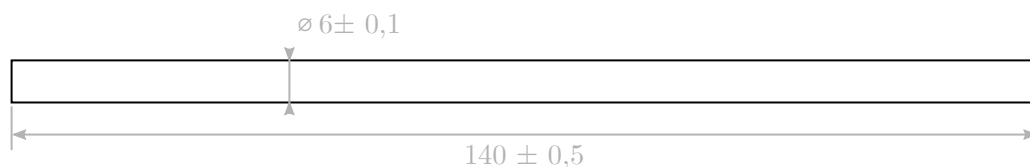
Dimensions géométriques des éprouvettes pour les essais de dilatométrie libre.
